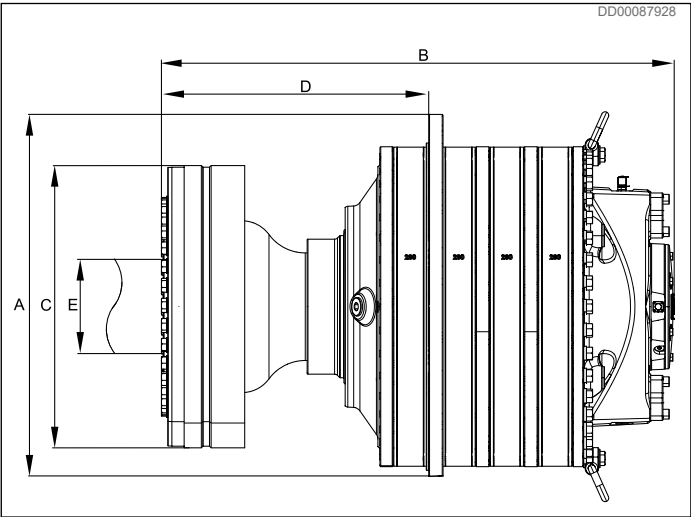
Motor CB 1120 con adaptador de acoplamiento
